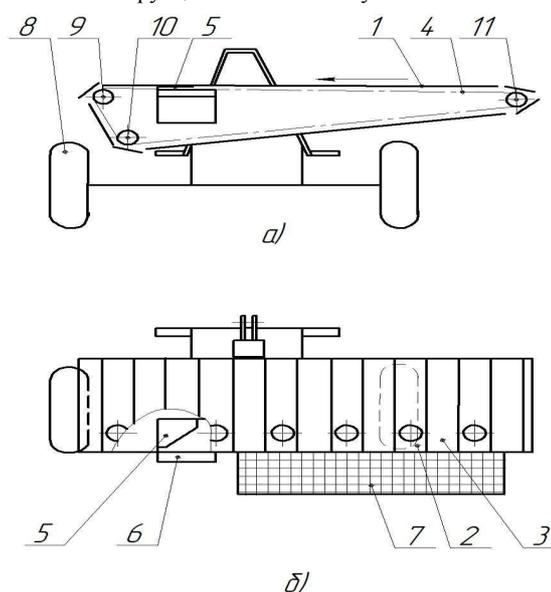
Схема стола доработки капустоуборочного комбайна: а) вид сбоку; б) вид сверху;
